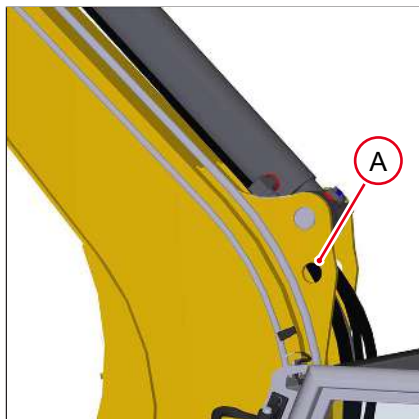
Olhais de elevação braço de elevação (representação de símbolos)
